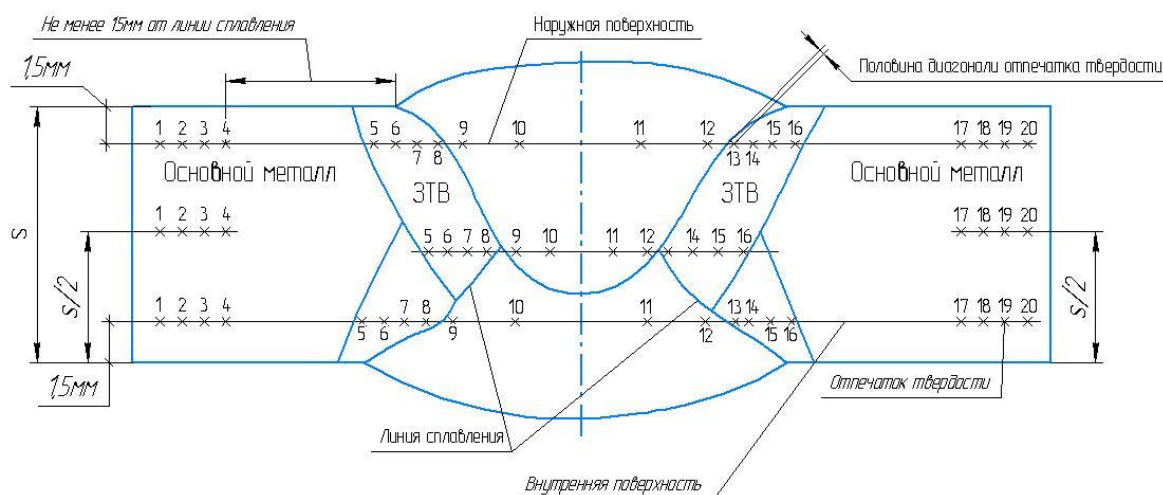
Схема контроля твердости на образцах кольцевых сварных соединений
